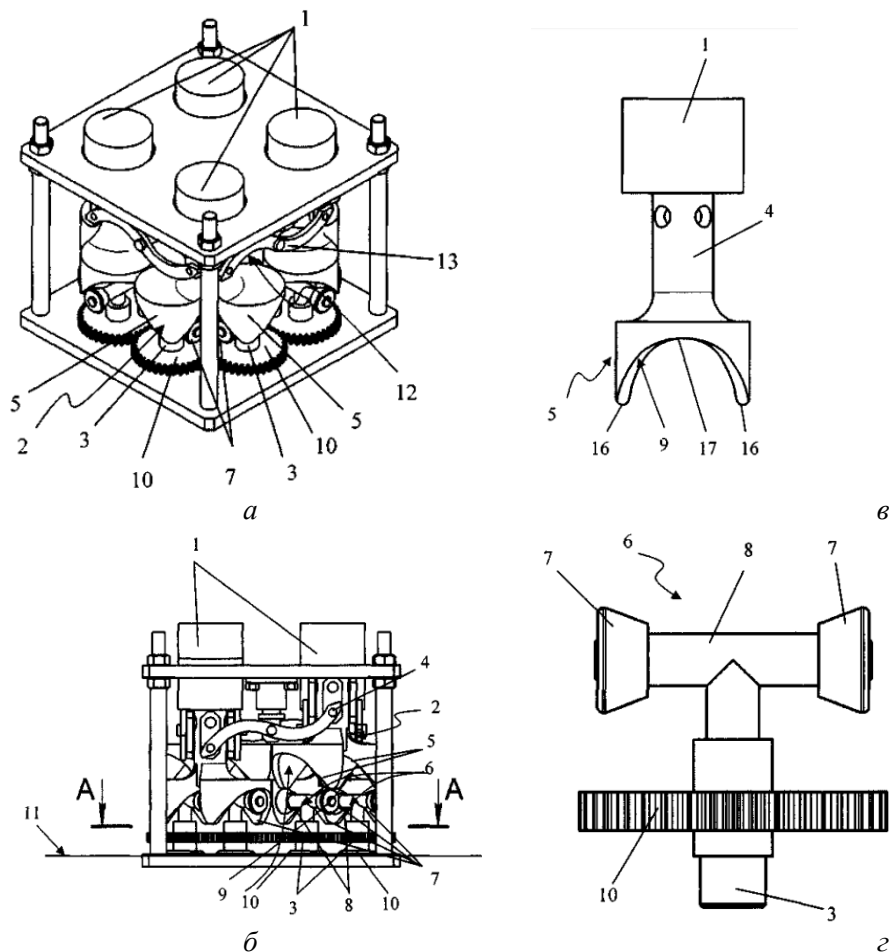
Схема конструкции двигателя с тангенциальным механизмом:
